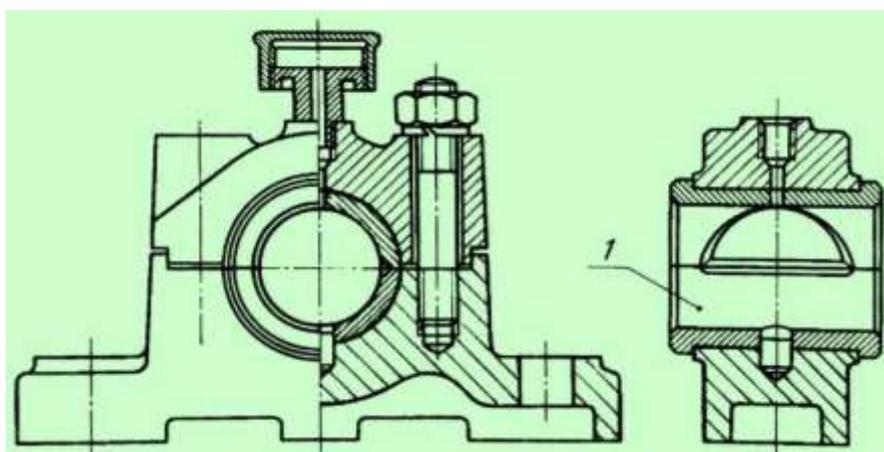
Подшипник с разъемным корпусом и вкладышем: 1 – вкладыш
